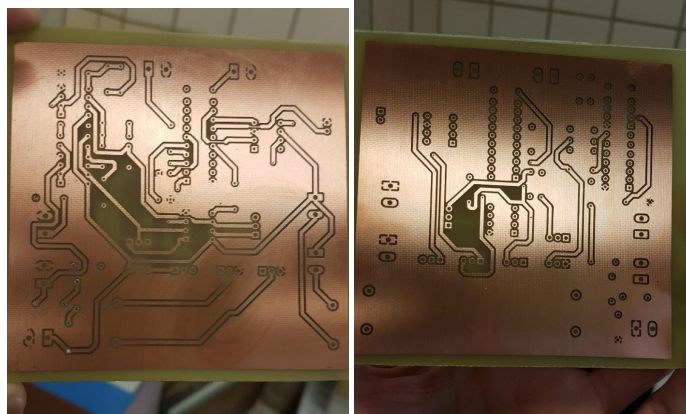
Parte superior e inferior del PCB antes de ser perforado.
